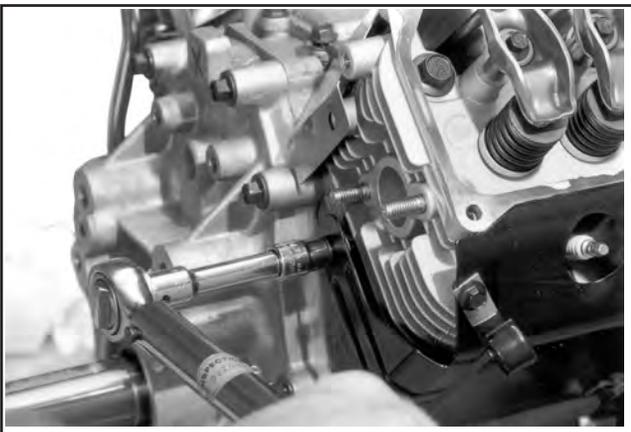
Die Befestigungsschrauben des Blechs anziehen.
